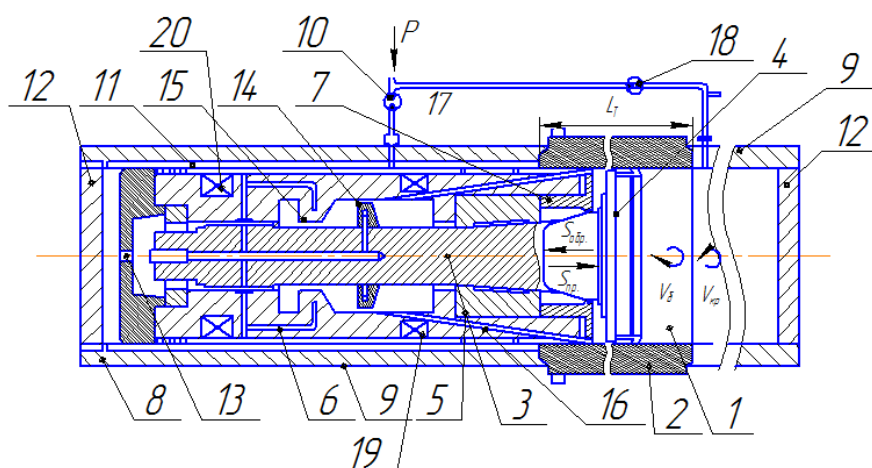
Малогобаритный станок с режуще-деформирующей пинолью для вихрефрезерования или внутреннего шлифования методом винтовой интерполяции
